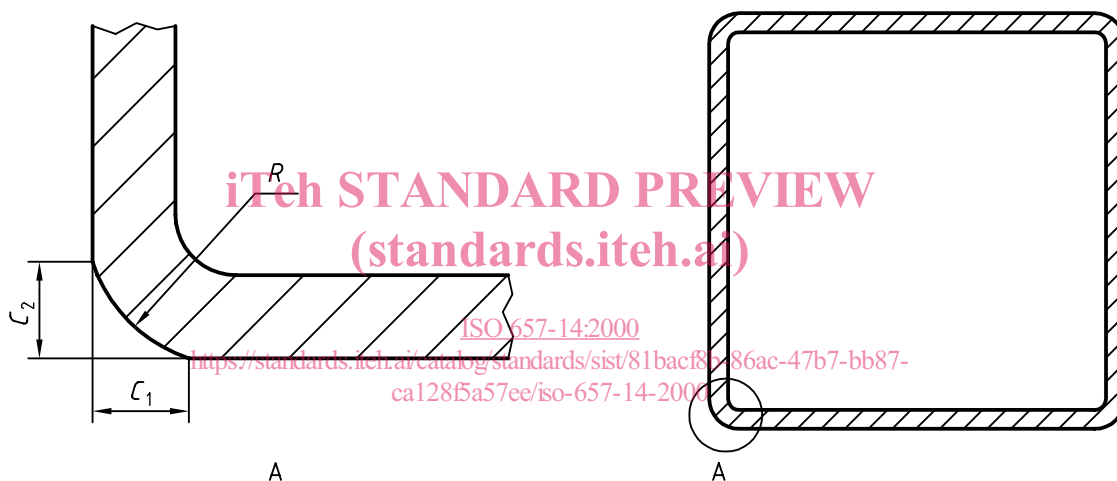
Profil d'arrondi externe d'un profil creux de section carrée ou rectangulaire
